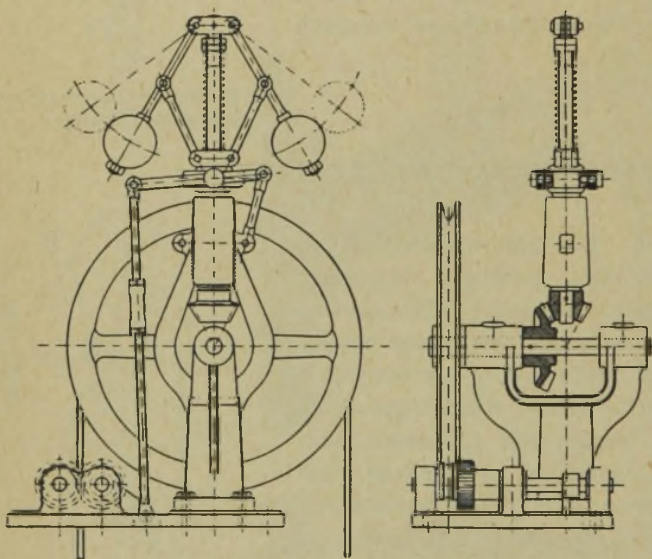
Mechanizm włączający z regulatorem odśrodkowym.
